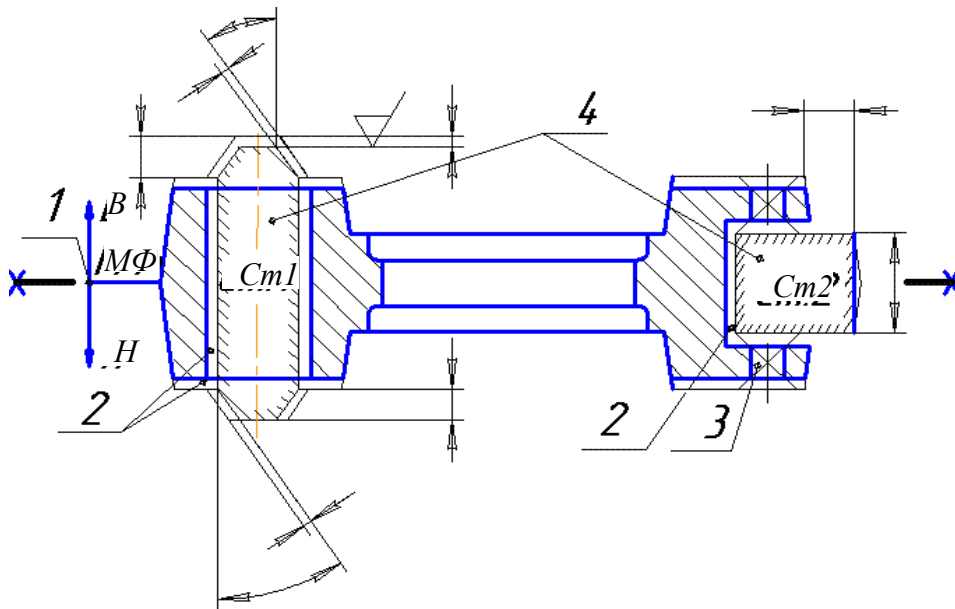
Кресленик «Елементи ливарної форми»
